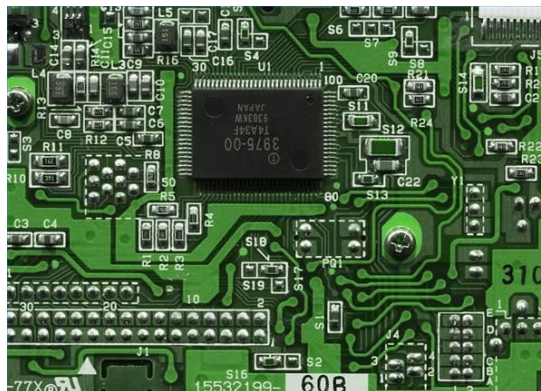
Conjunto de componentes SMD incorporados a una placa PCB.
